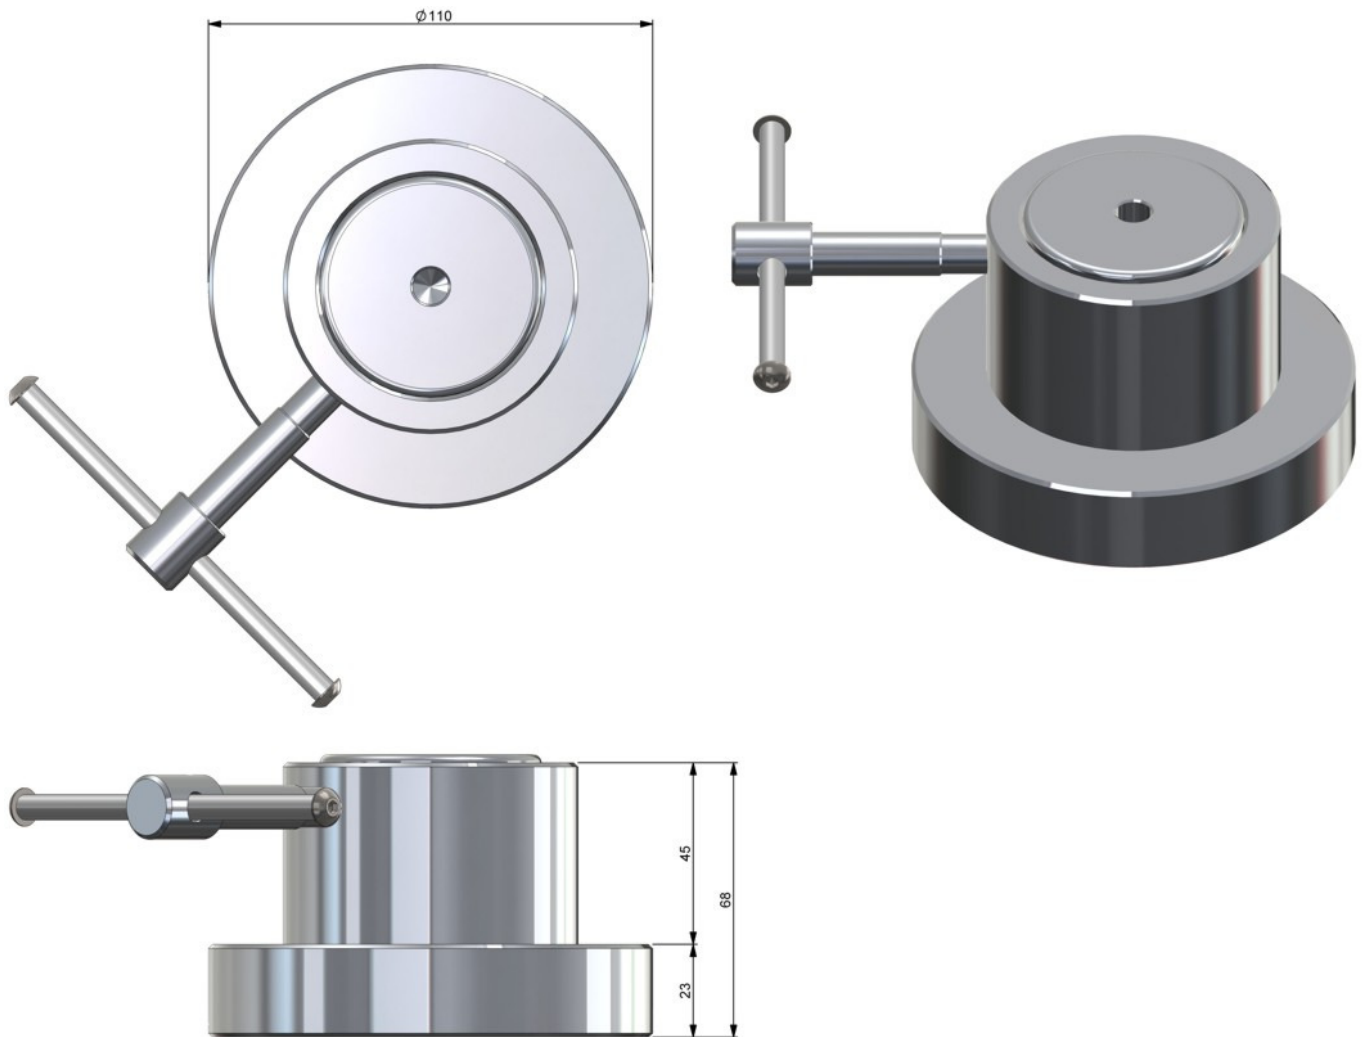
Dimensionamento para montagem da Flange (Cotas em milímetro)
